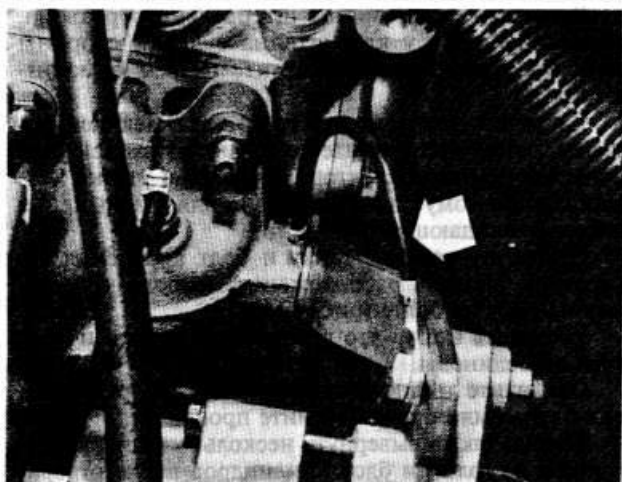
Провод заземления на массу, закрепленный с верхней стороны генератора — двигатель с одноточечным впрыском топлива
